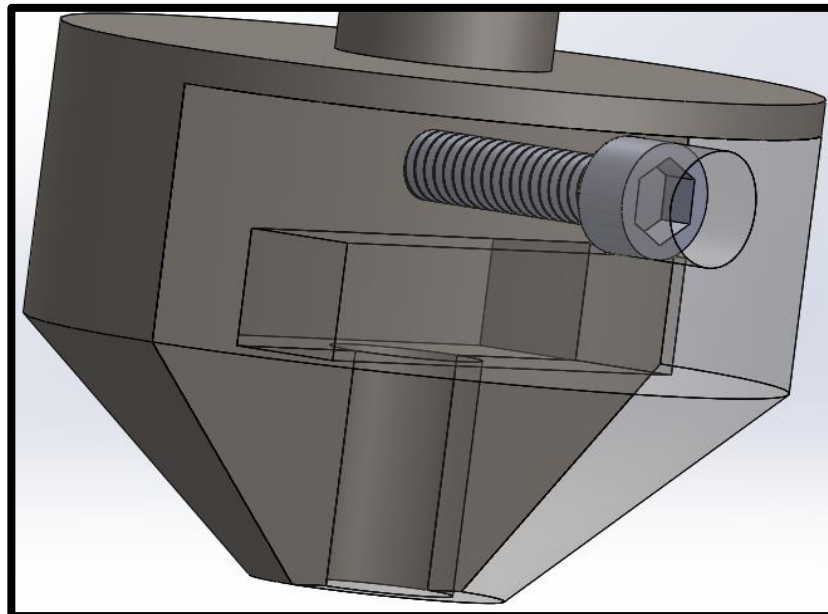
Detalle del conjunto ensamblado de ambas partes de la mordaza y el tornillo. Fuente: Propia.
